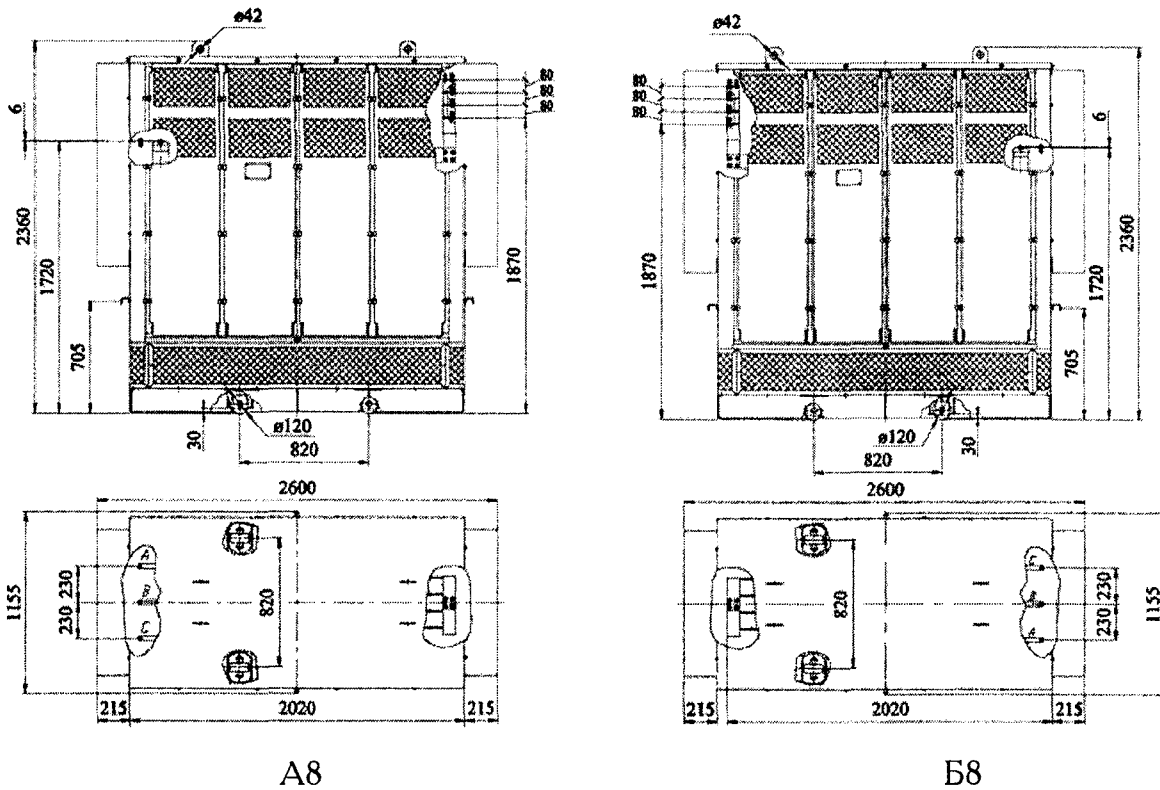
Габаритные, установочные, присоединительные размеры трансформатора ТСЗФ-630/20 У3 (сторона подключения: А8 - левая, Б8 - правая)
